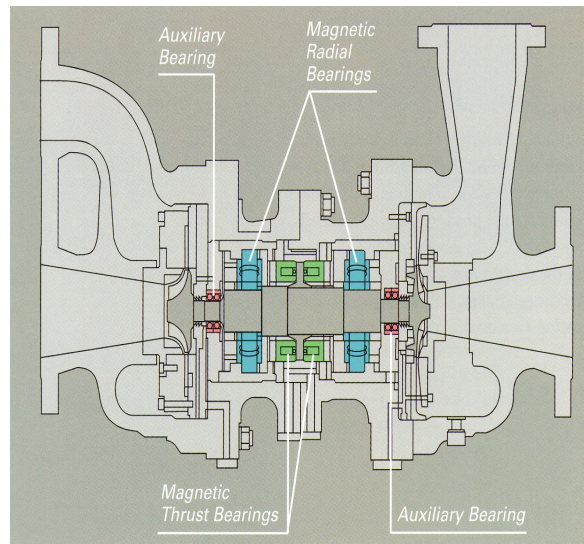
Querschnittszeichnung einer mit Hilfe von geregelten Elektromagneten unterstützten Welle einer Turbomaschine
